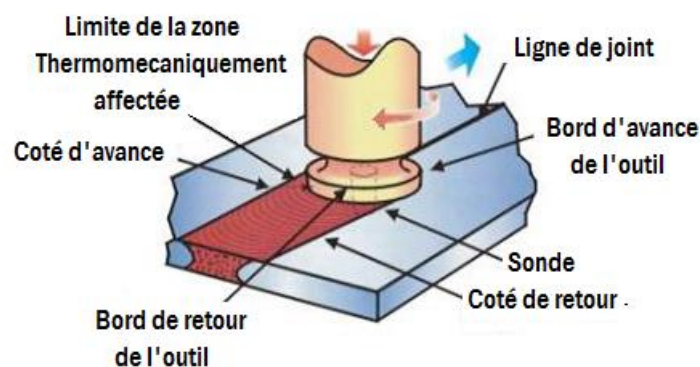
Représentation schématisée du procédé de soudage par friction-malaxage [6].
